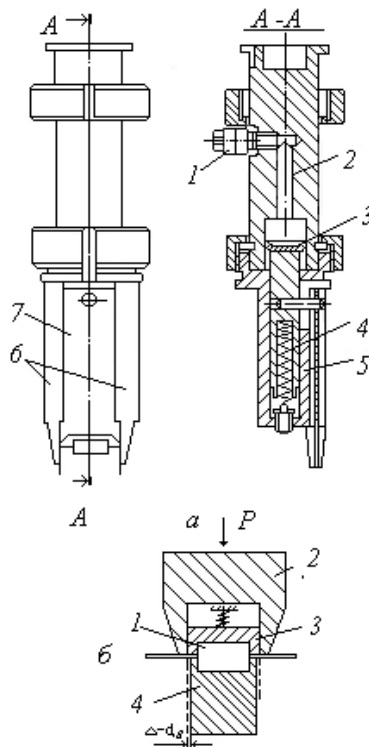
Устройство захвата резисторов: а – общий вид; б – расчетная схема:
